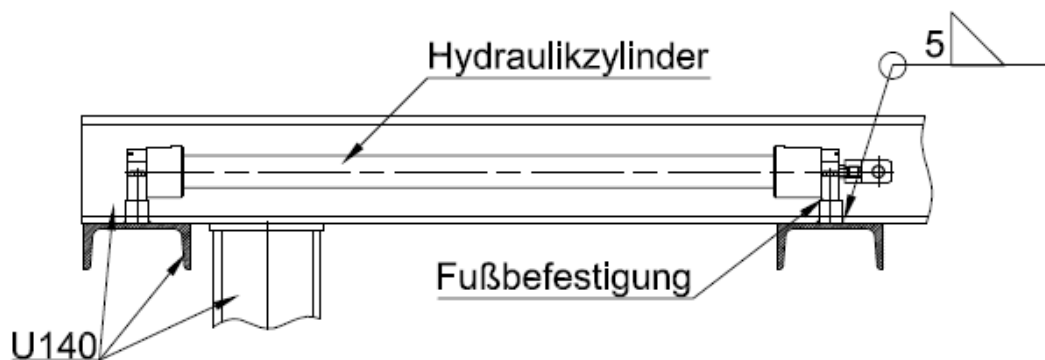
BG11; Detail Hydraulikzylinderbefestigung
